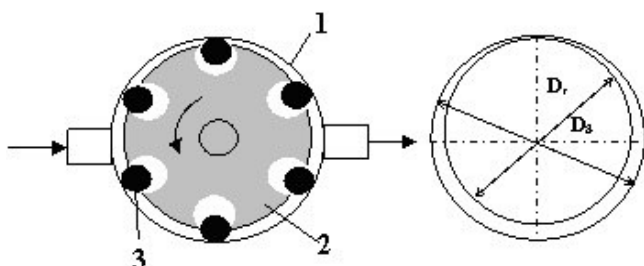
Pompă cu role: 1- carcasă; 2- tambur; 3- role
